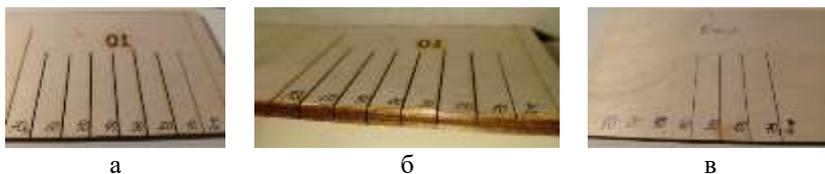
Образец после испытаний (скорость перемещения лазерного луча - 10 мм/с): а - лицевая сторона; б – кромка; в – обратная сторона
